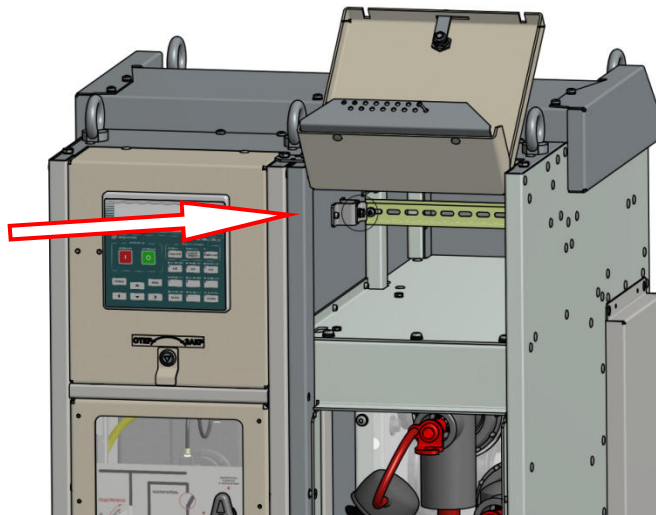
Усатновка держателя TER_SGunit_Holder_58
